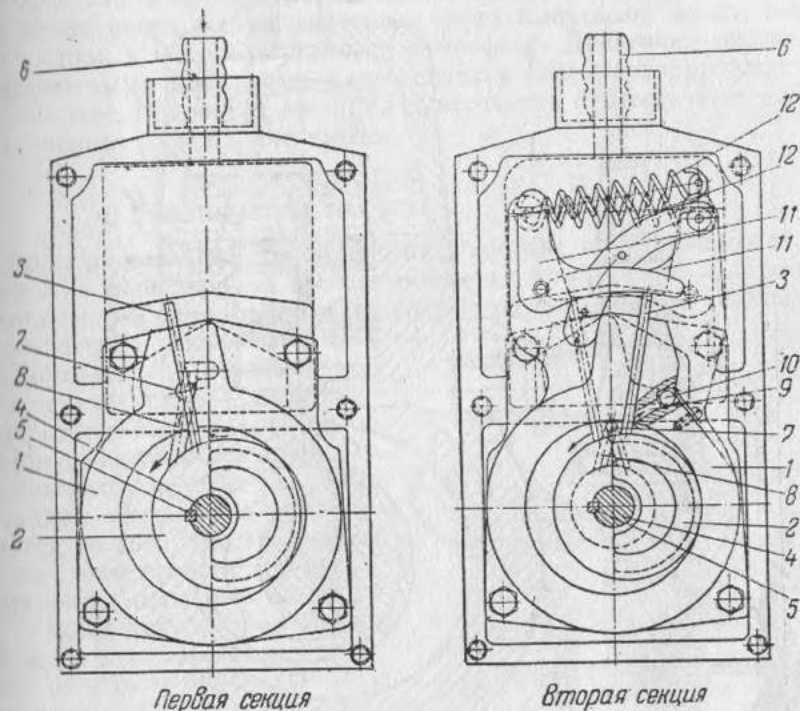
Двухступенный пластинчато-статорный насос ВН-461.
